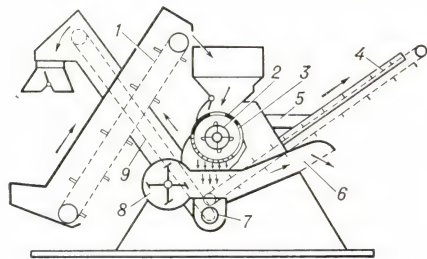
Схема кукурузной молотилки: 1 — питающий транспортер; 2 — молотильный барабан; 3 — цилиндр с отверстиями; 4 — транспортер стержней початков; 5 — решётчатый стан; 6 — рукав для вывода лёгких примесей; 7 — зерновой шнек; 8 — вентилятор; 9 — зерновой элеватор.
